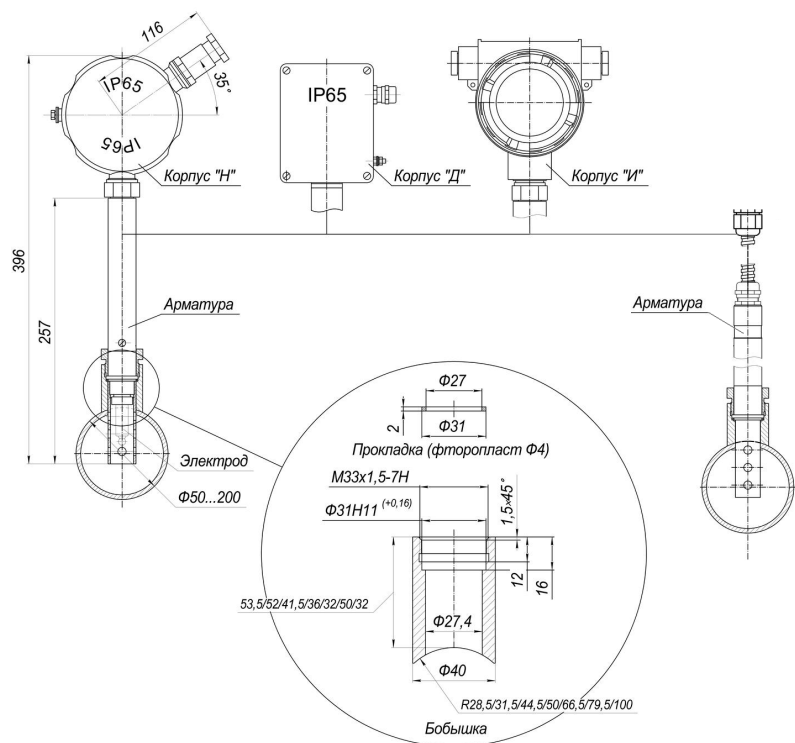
Крепление трансмиттера на трубопроводе с помощью арматуры [АПН-3.1](#)
